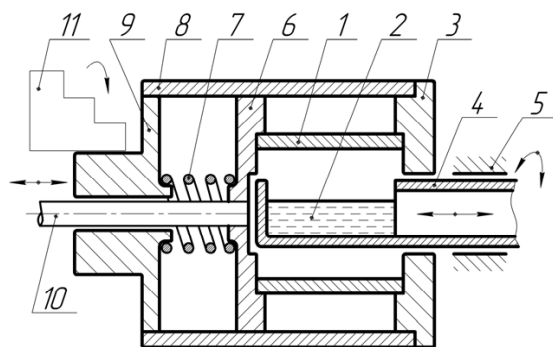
Схема центробежной заливки эластомера: 1 – восстанавливаемая деталь; 2 – раствор эластомера; 3 – наружный установочный диск; 4 – дозирующая трубка; 5 – направляющие; 6 – нажимной диск; 7 – пружина; 8 – защитный кожух; 9 – основание корпуса; 10 – шток для отвода нажимного диска, 11 – кулачки патрона токарного станка
